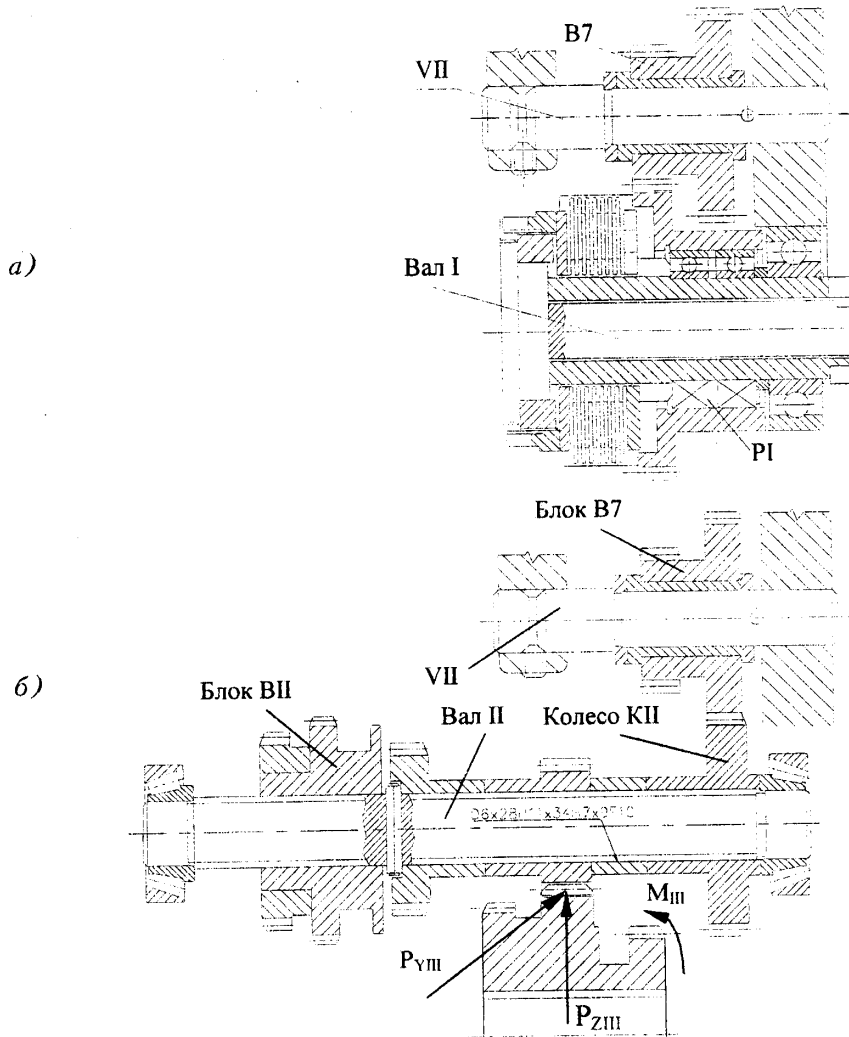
Конструктивна схема кінематичного ланцюга групи реверса:
